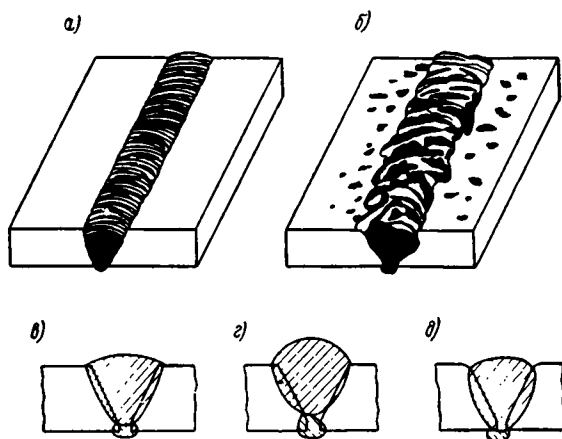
Качество сварных соединений при заварке трещин с V-образной разделкой:
